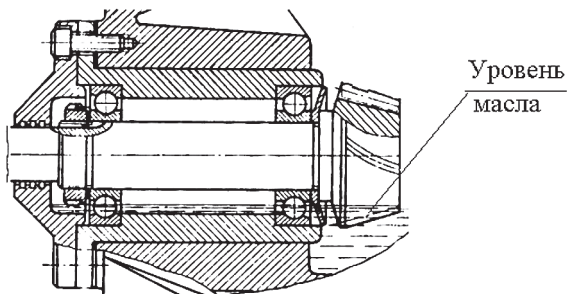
Конструкция узла, выполненная по схеме Г
